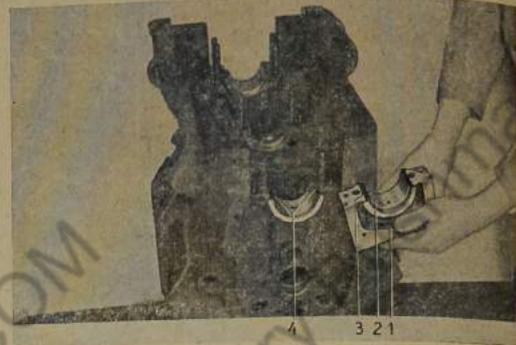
Untere Lagerschale in Lagerdeckel einschlagen
